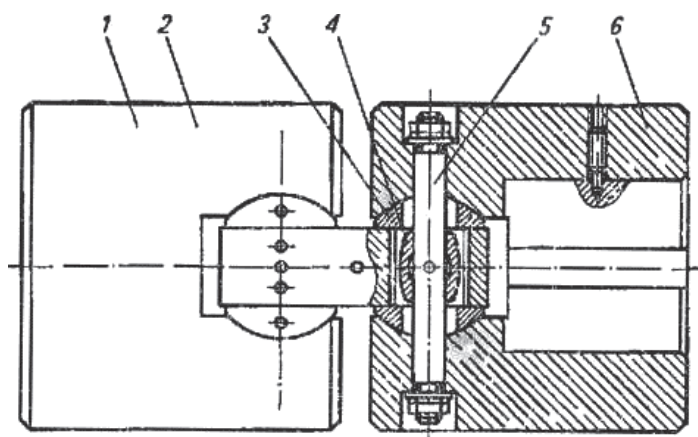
Шарнирная муфта для привода лопастного вала резиносмесителя
